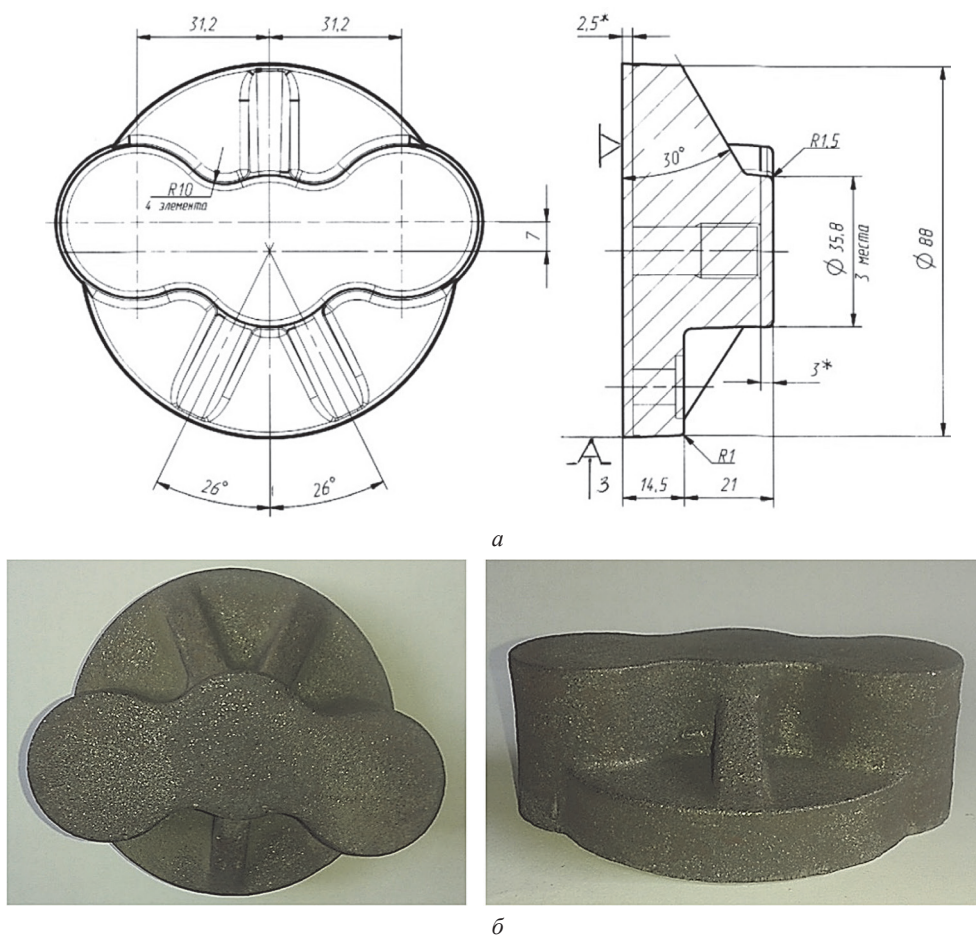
Чертеж отливки «Крышка MRR» (а) и вид отливок, полученных в составе опытной партии (б)
